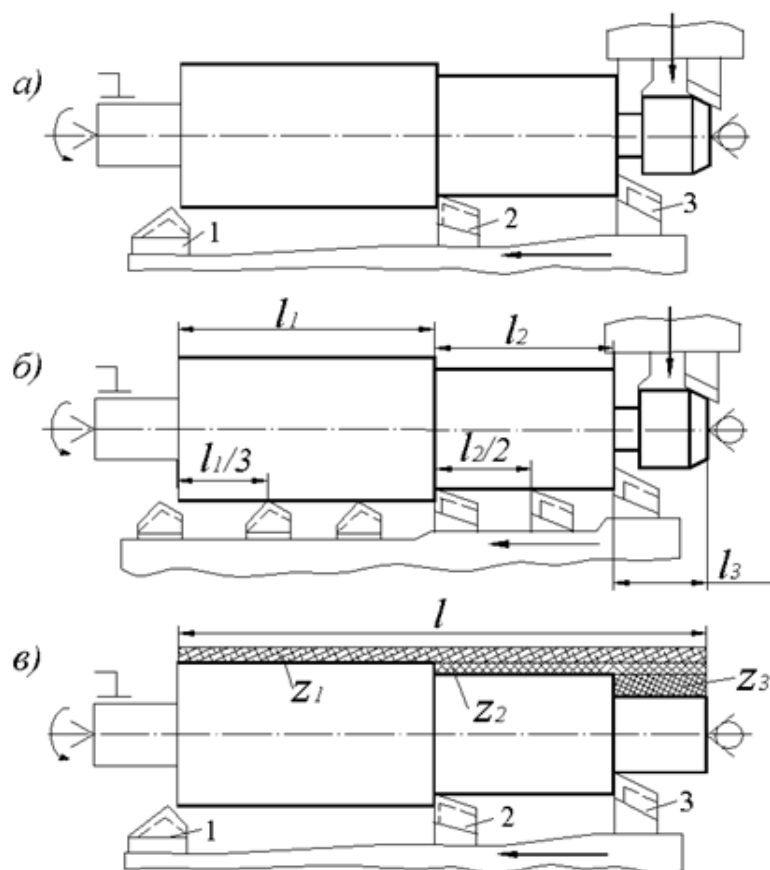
Схемы точения ступенчатого вала на многолезцовом станке
